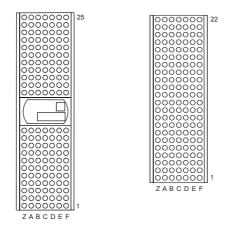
Steckverbinder P1 und P20 Front (Ansicht: Steckseite)
